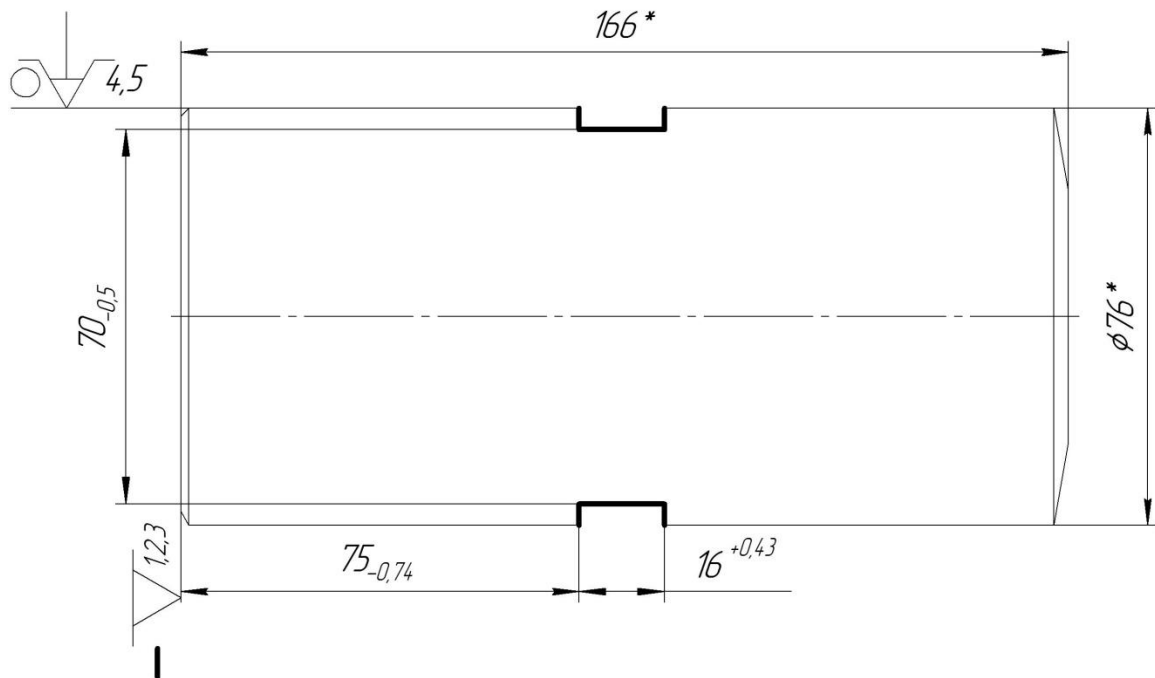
Схема базування заготовки на фрезерній операції (перший варіант)
